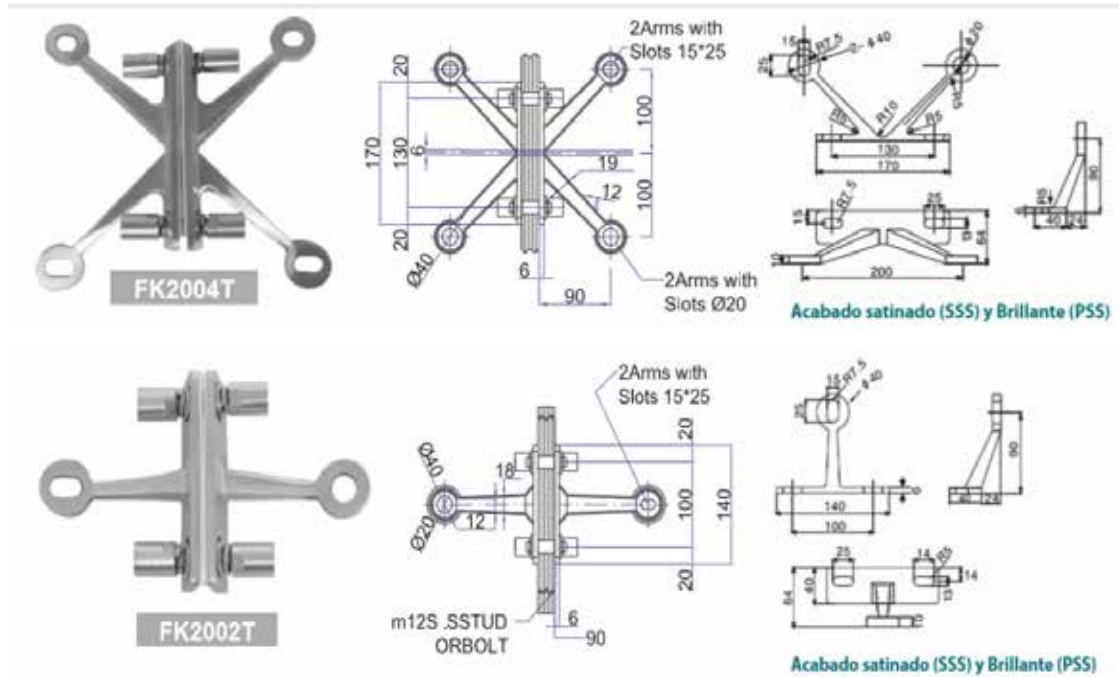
Detalle del Spider de Curtain Wall. Fuente: vidriosbrenes.com(2021)
